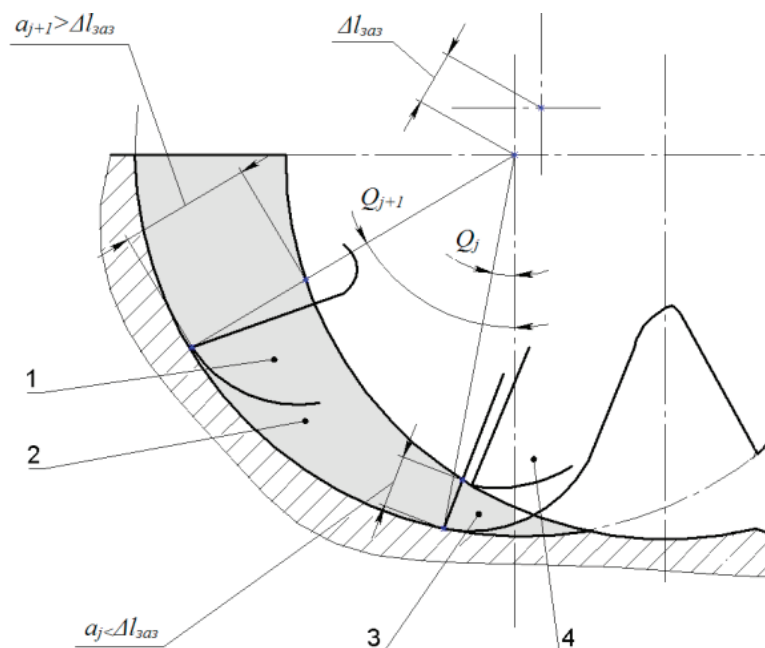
Изменение длины дуги контакта, вследствие наличия зазоров в кинематических цепях оборудования: 1 — зуб фрезы; 2 — срезаемый слой материала обрабатываемой поверхности; 3 — положение зуба инструмента в случае отсутствия зазоров в цепях станка; 4 — реальное положение зуба инструмента вследствие отжатия от обрабатываемой поверхности при толщине срезаемого слоя меньше суммарной величины зазоров
